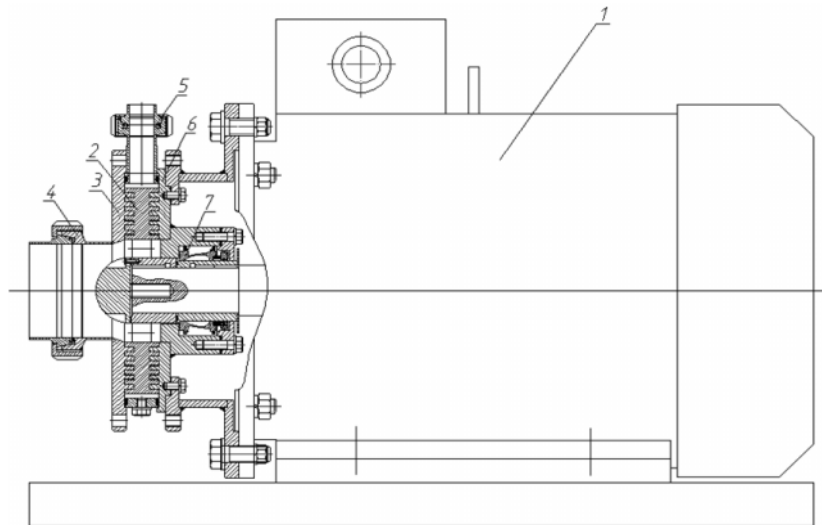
Типова конструктивна схема роторно-динамічного агрегату-гомогенізатора
